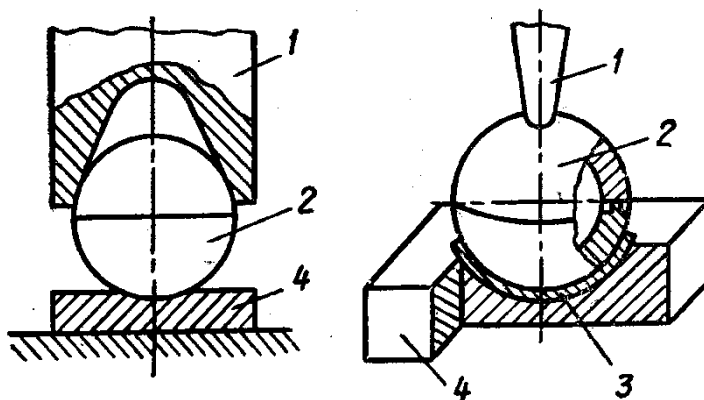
Опори для зварювання об'ємних деталей: 1-хвилевід; 2-виріб; 3-гумова прокладка; 4-опора.
